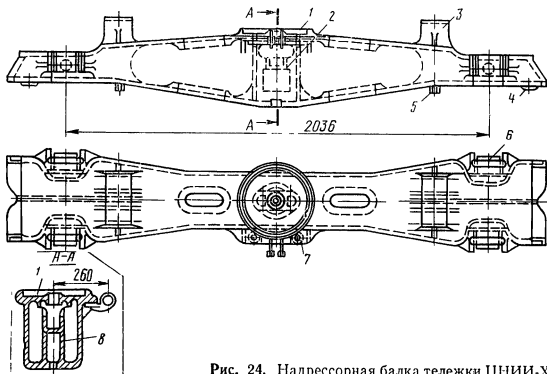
Наддрессорная балка тележки ЦНИИ-ХЗ-О
